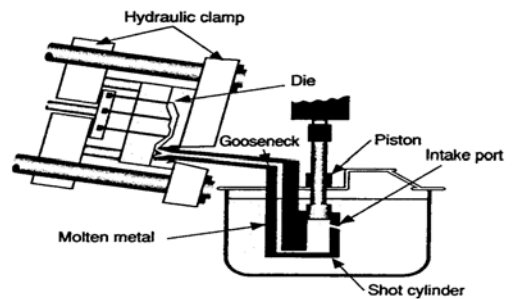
(b) Hot Chamber Die Casting [3] 熱室法
